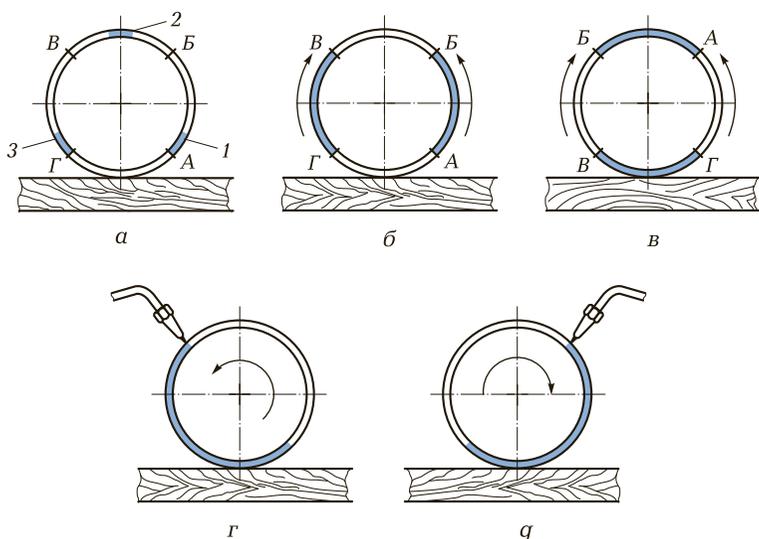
Последовательность сварки стыков труб с поворотом:
